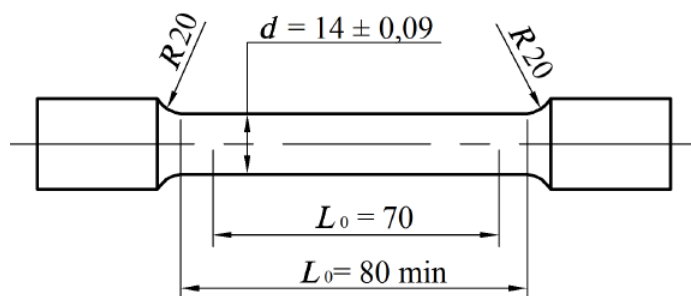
Образец для определения прочности отливок из высокопрочного чугуна
